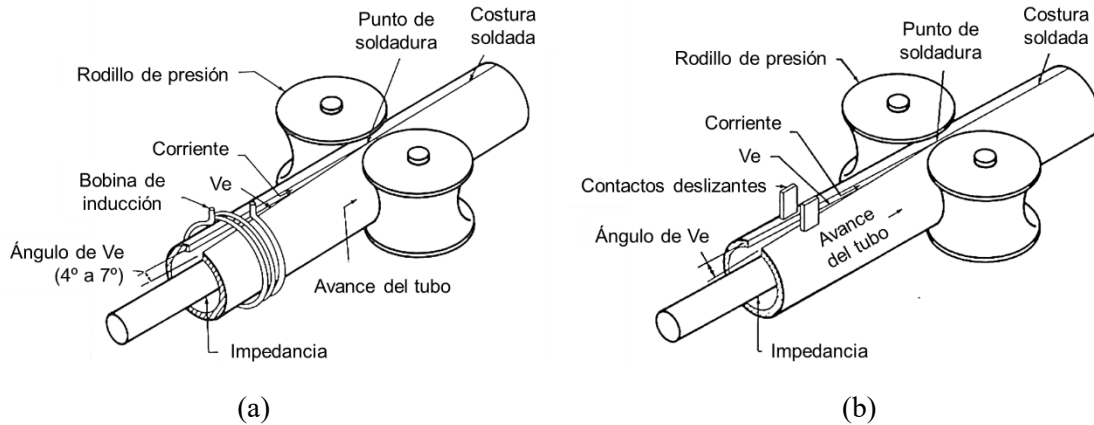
Sistemas de fabricación de tubos por soldadura de alta frecuencia (SAF): (a) soldadura de alta frecuencia por inducción y (b), soldadura de alta frecuencia por contactos [14].
